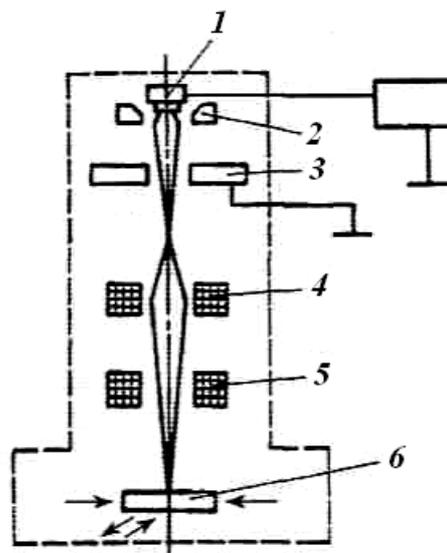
Схема установки для электронно-лучевой сварки:
